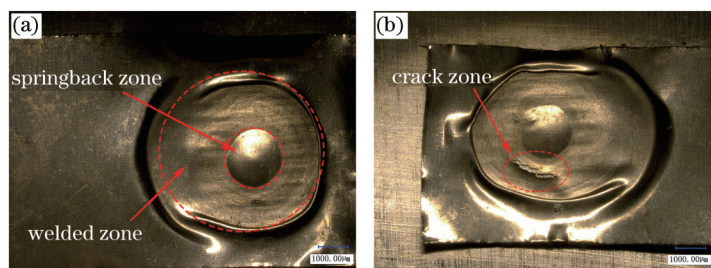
复板飞行距离为0.6 mm时焊点形貌图。(a) 焊接试样表面形貌; (b) 复板破裂失效
